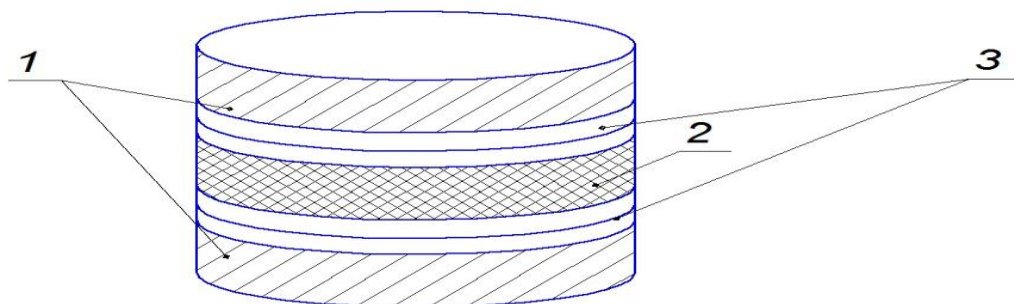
Схема слоистой прессованной порошковой заготовки для проведения экспериментов:
